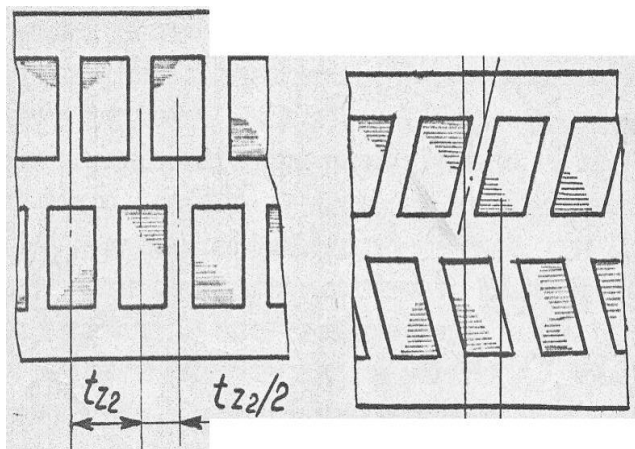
Схема двухполюсного ротора с дополнительным скосом пазів в кожному з пакетів
